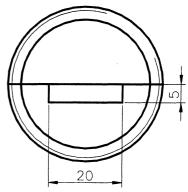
Фильера для литья полосы размером 20x5 мм (вид со стороны тянущих валков)
